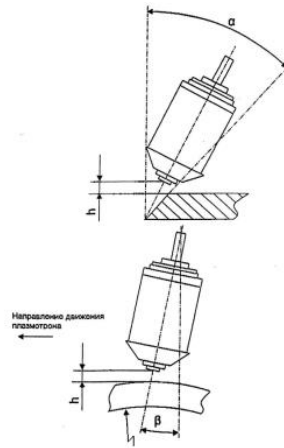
Схема установки плазмоторна на трубе при полуавтоматической резке.
